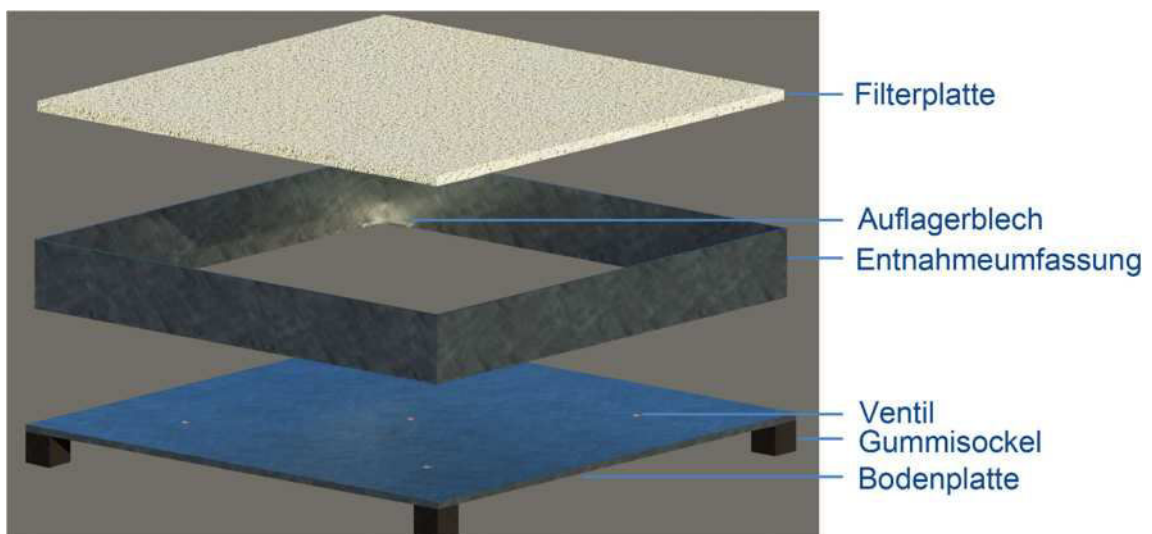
Explosionszeichnung Entnahmevorrichtung
